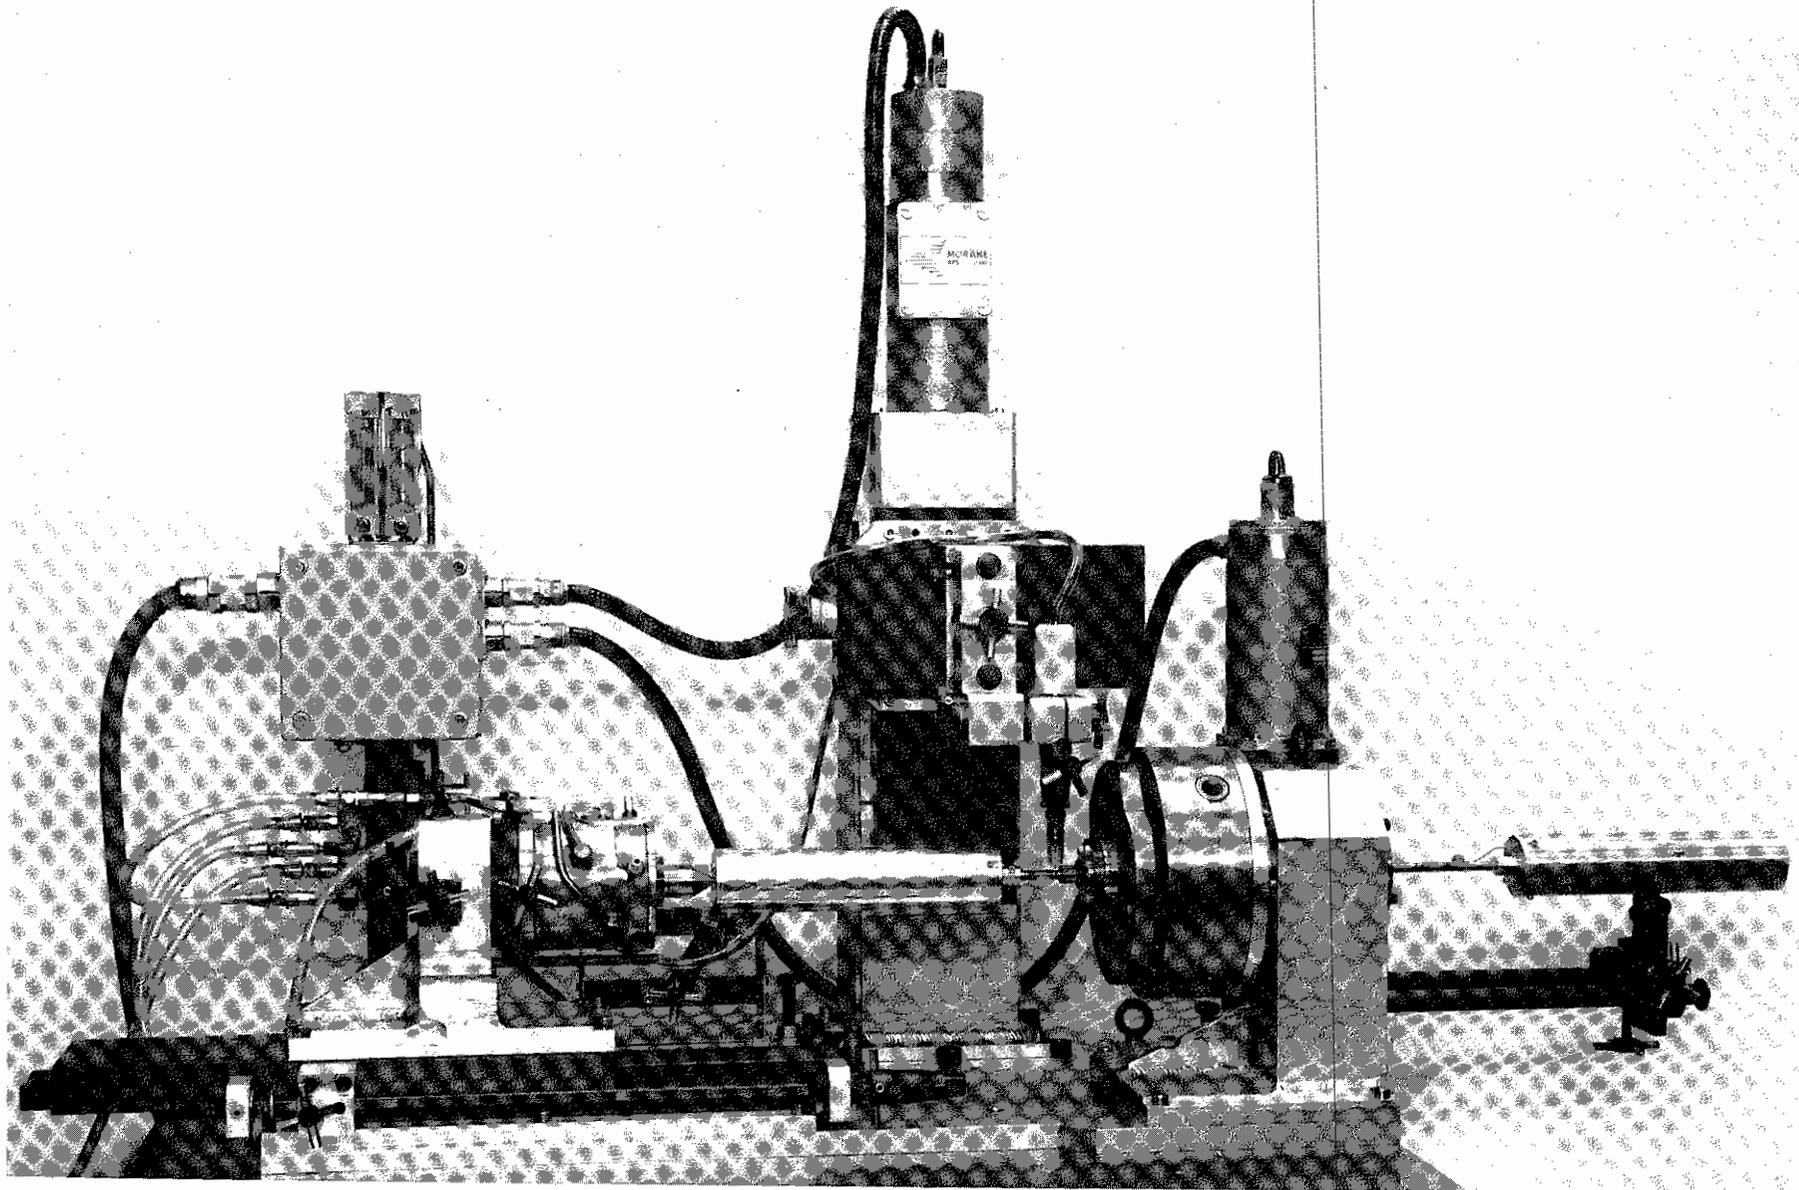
MACHINE D'USINAGE - MONTAGE DU DISPOSITIF ENDOSCOPIQUE
